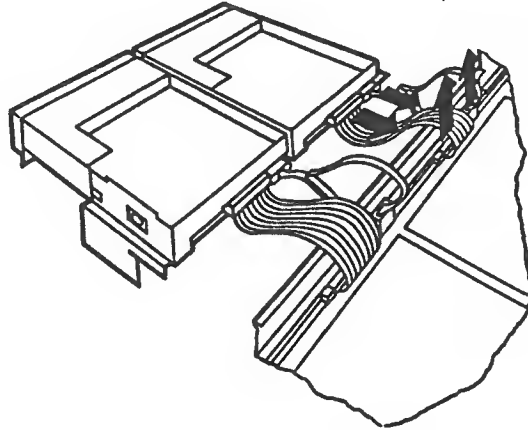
Kabel vom Diskettenlaufwerk entfernen
